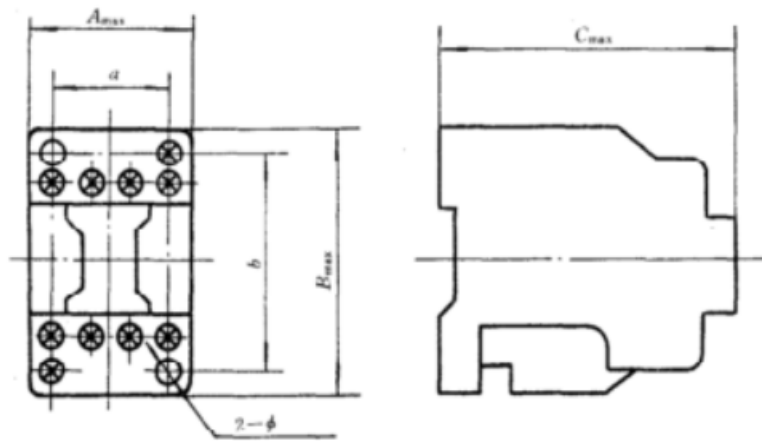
CJX 5-9~16 型交流接触器外形尺寸与安装尺寸
